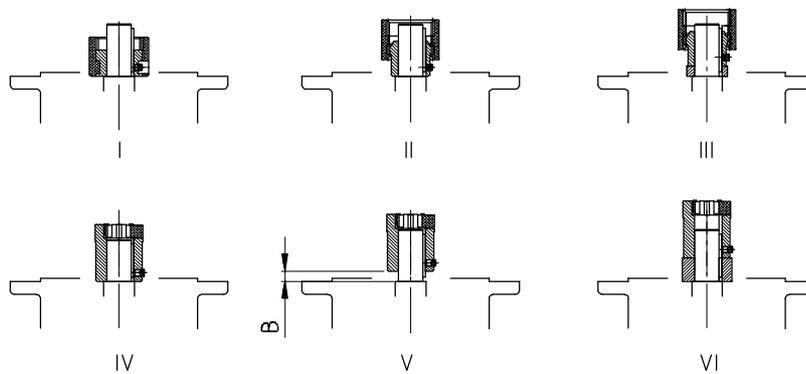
Установка муфты на вал двигателя при различных конструкциях муфты
